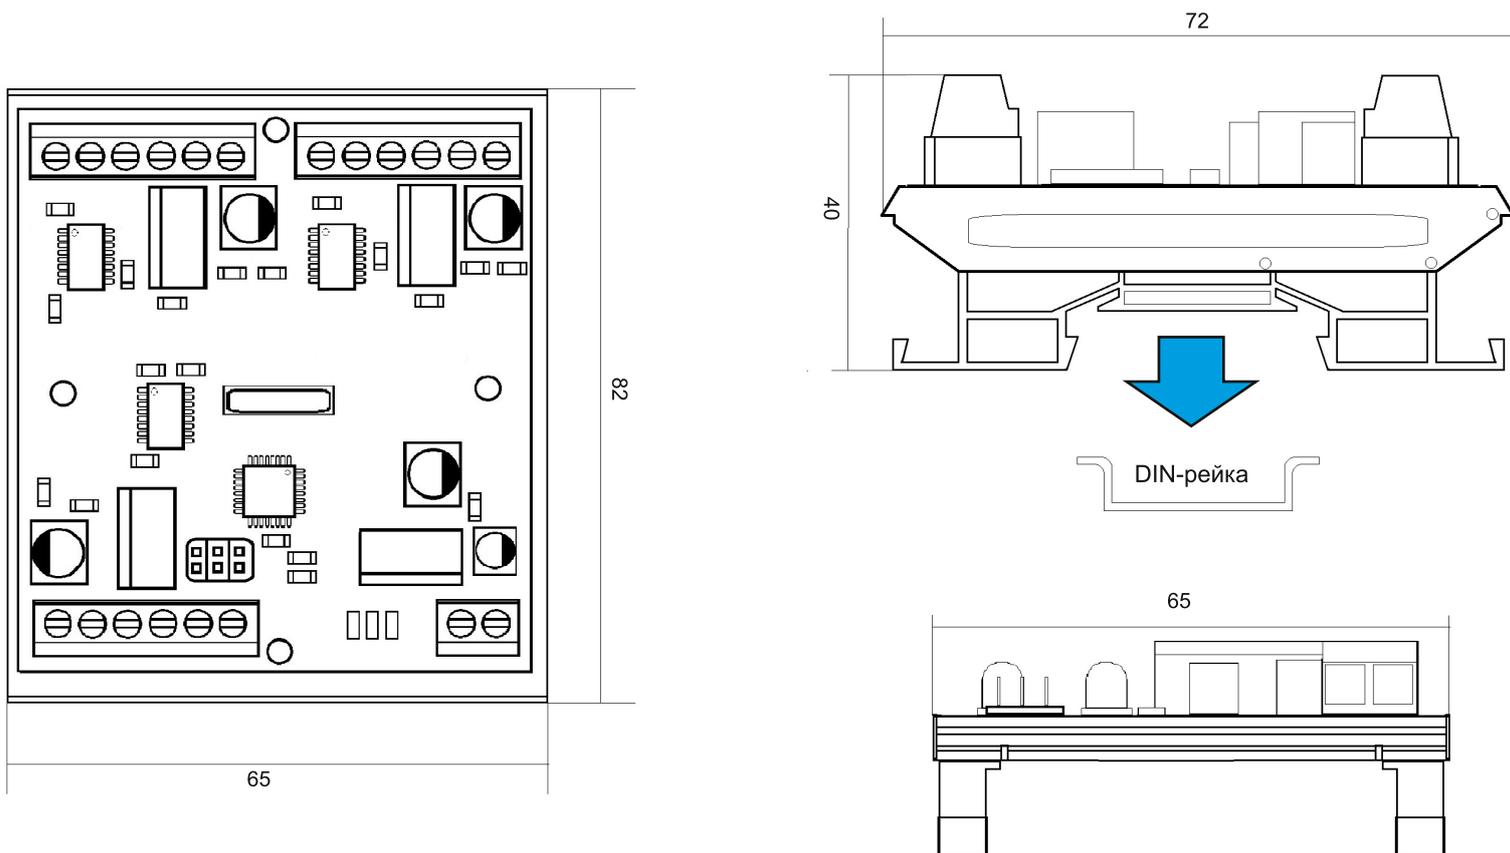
Габаритные чертежи модуля с DIN-креплением.
